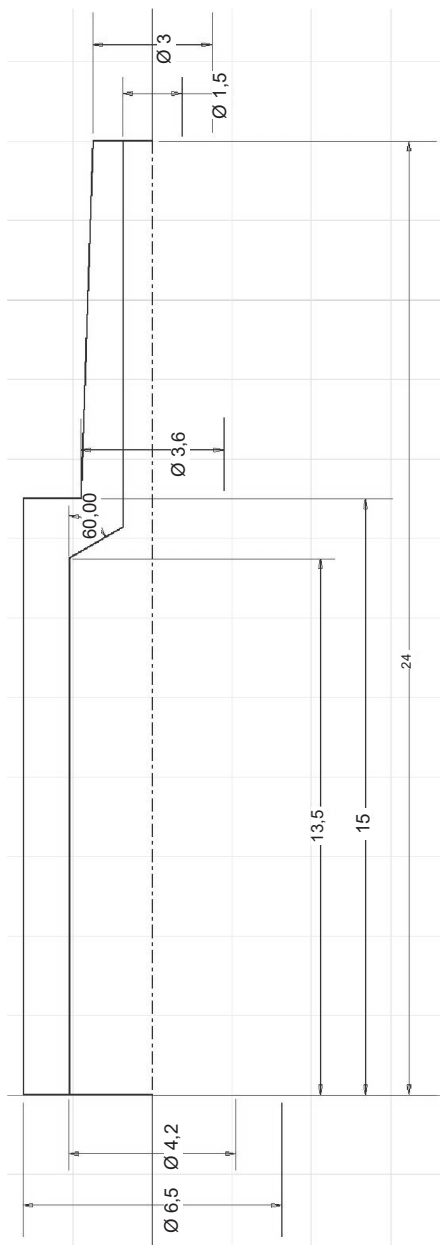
Базовый эскиз модели переходной канюли с исполнительными размерами
